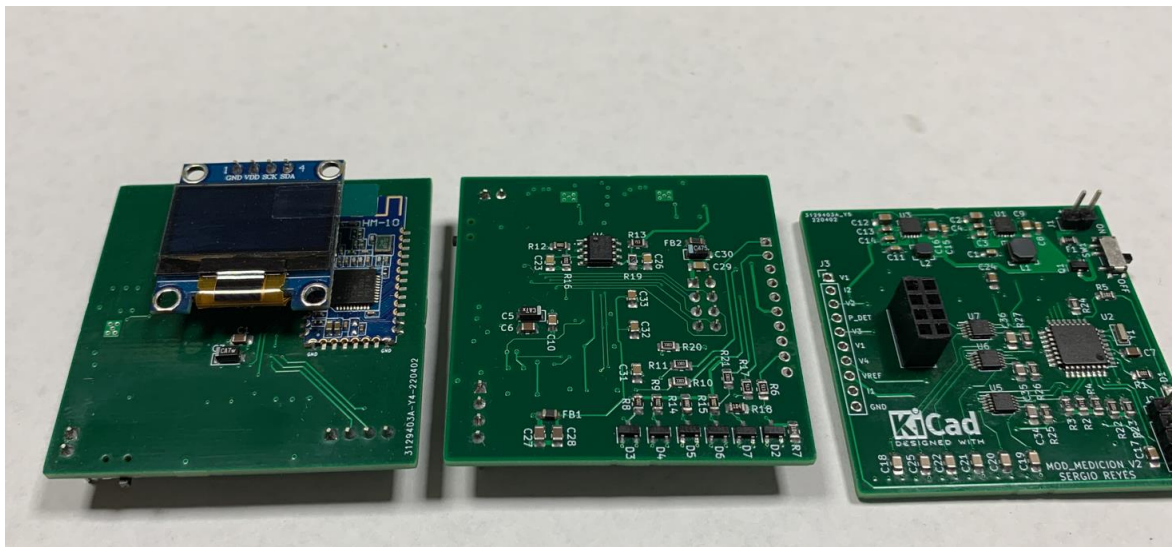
Proceso de Soldadura Procesadores ATMEGA328
